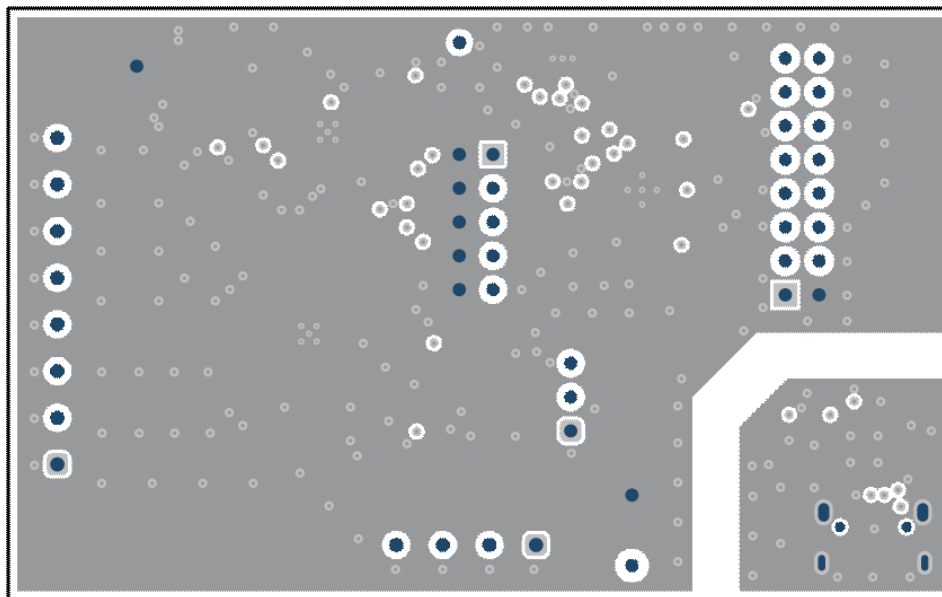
SNSR-DUAL-ADC-EVM PCB 布局 - 接地层 (第 2 层)
